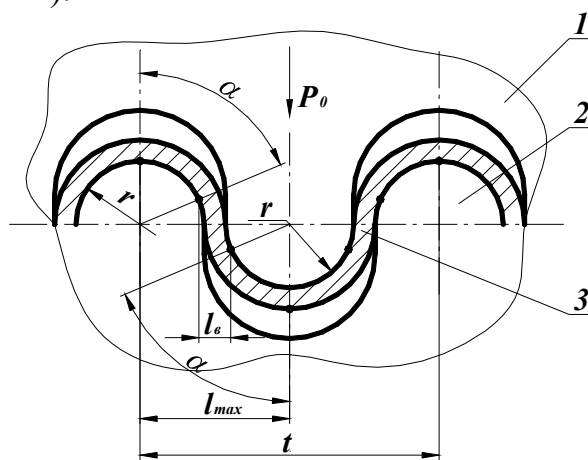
Розрахункова схема гофроутворення формувальними інструментами-колесами із спеціальним закругленим профілем зубів.
